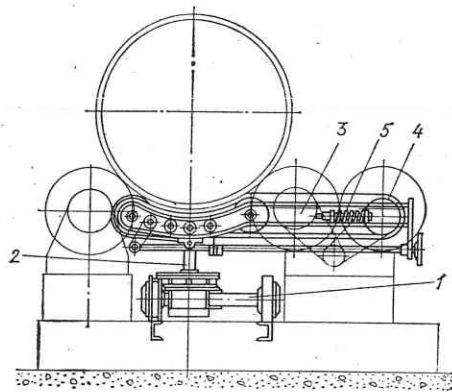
Флюсовая подушка для сварки кольцевых швов:
